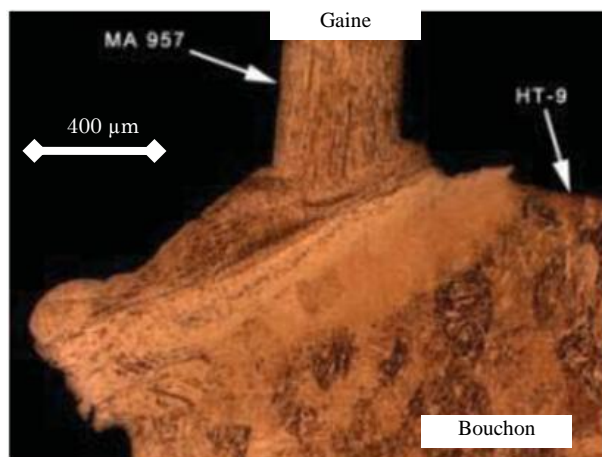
Macrographie d'une soudure réalisée par soudage par résistance entre MA957 (gaine) et HT9 (bouchon) [56]
